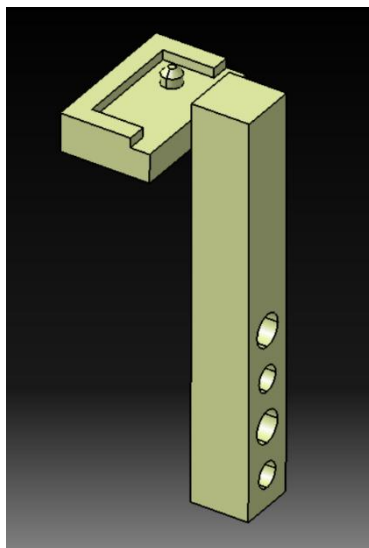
TORRE DE SOLDADURA #1
